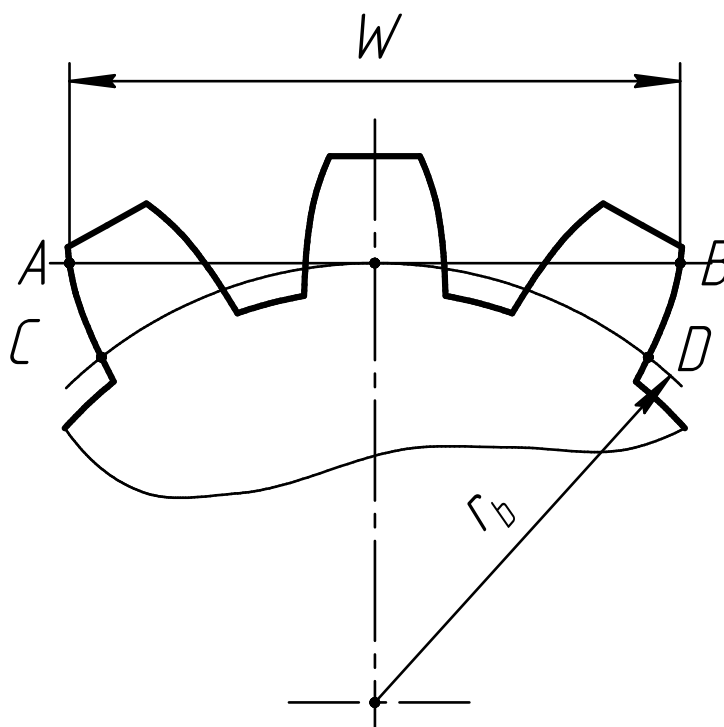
Длина общей нормали зубчатого колеса
